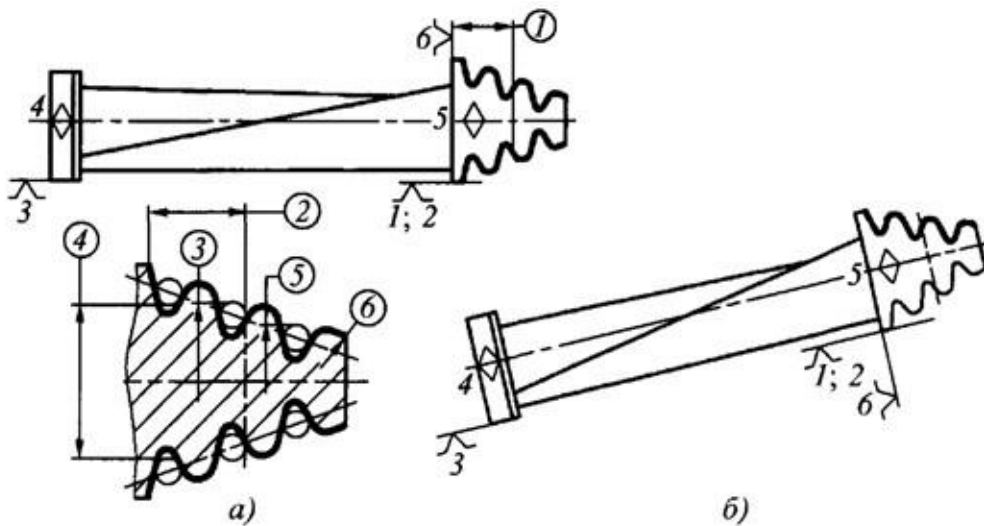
двобічна (а) й однобічна (б) схеми обробки замка лопатки.
